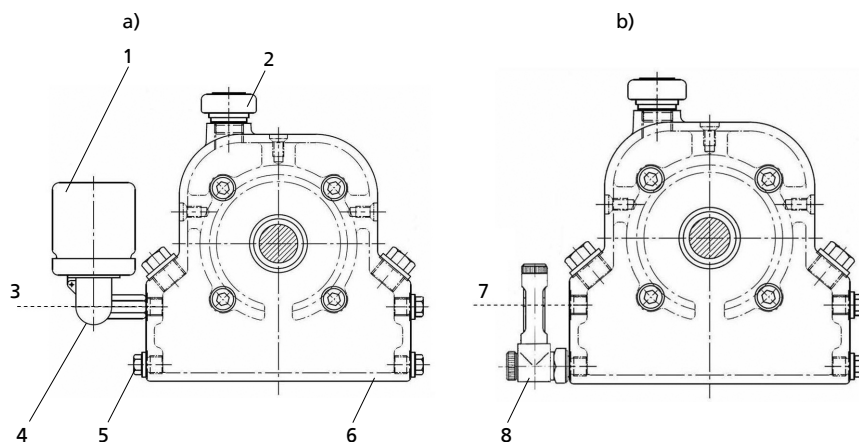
а) Корпус подшипников с регулятором уровня масла - б) Корпус подшипников с указателем уровня масла
